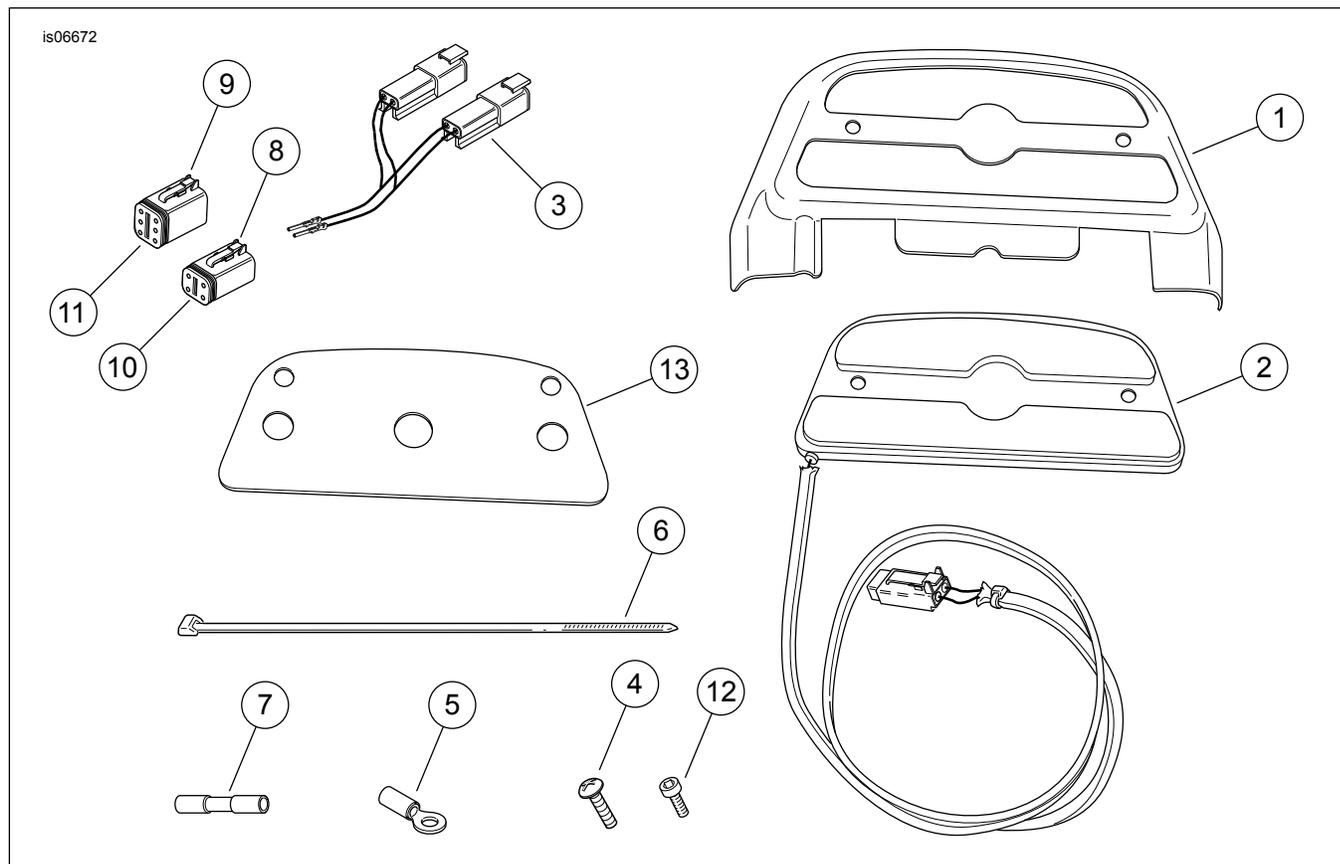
Peças de reposição: Tampas do estribo iluminado do passageiro
